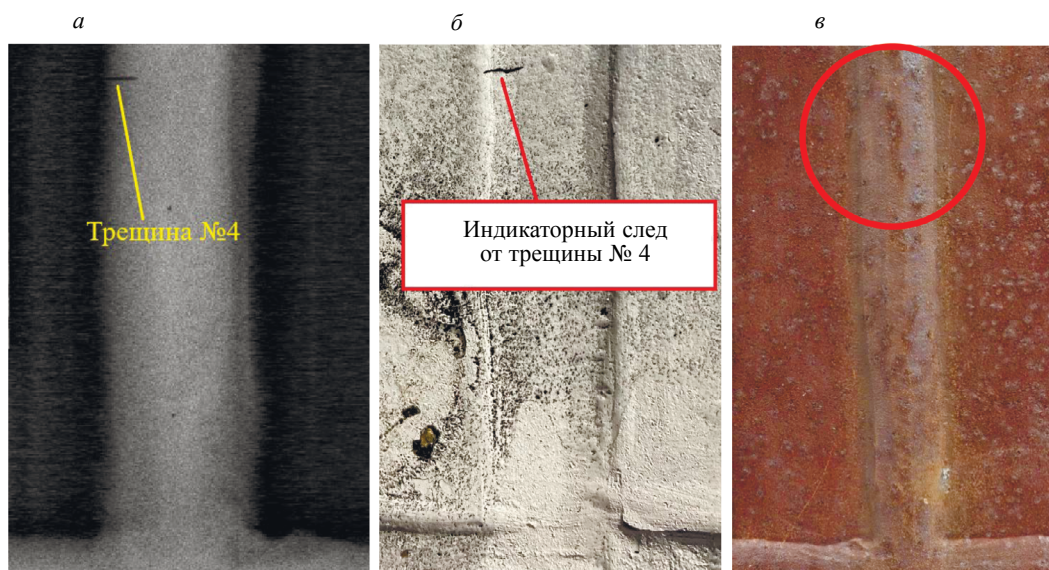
Трещина № 4 в вертикальном сварном шве стенки РВС: радиографический снимок (а); результат магнитопорошкового контроля (б); внешний вид сварного шва (в).
